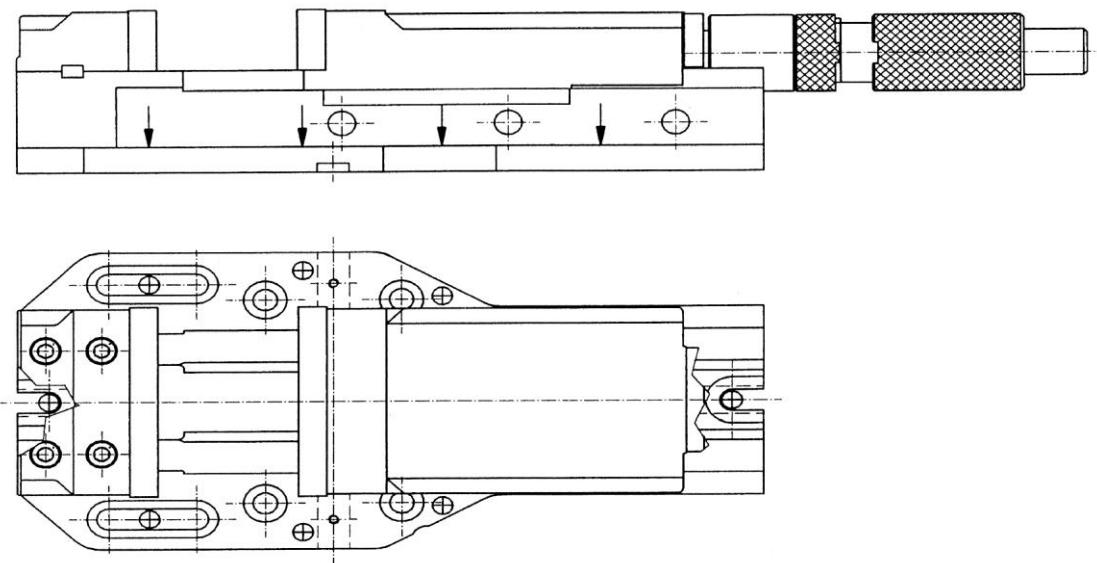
Empfohlene Schraubstockbefestigungspunkte am Maschinenwerkzeugtisch mit Befestigungsschrauben und Druckösen.
